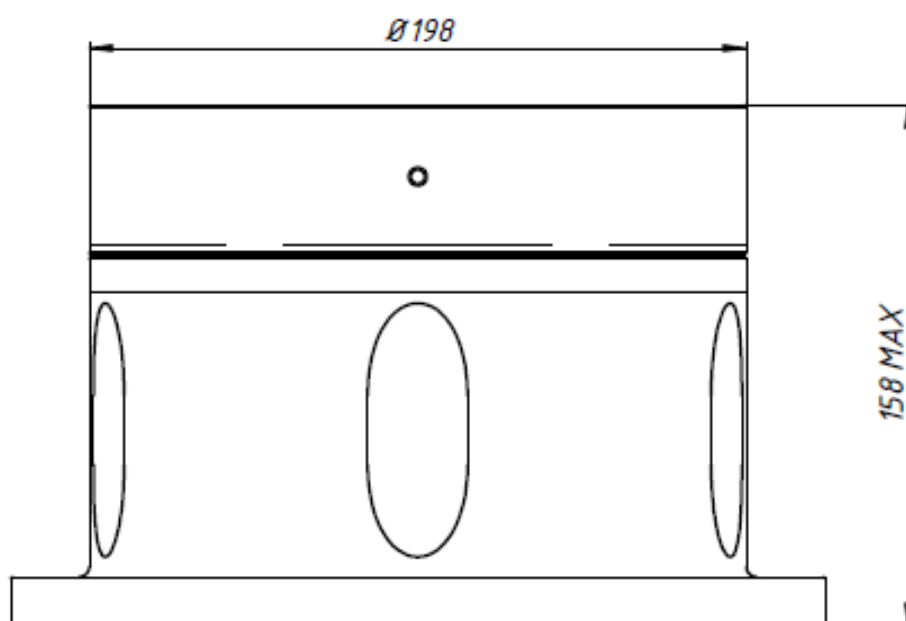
Габаритные размеры опорно-поворотного устройства
